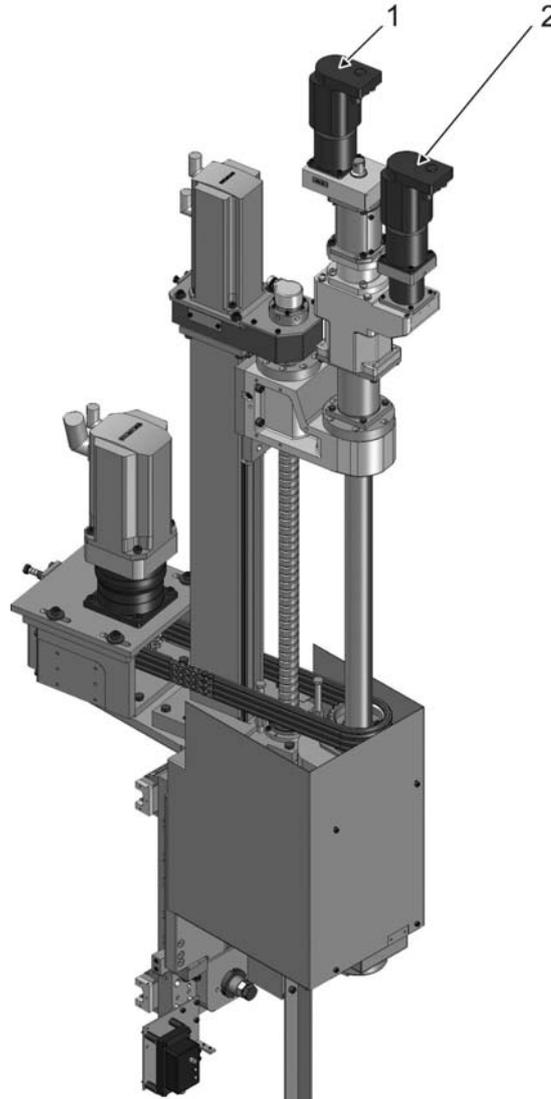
Spindleinheit VSM mit einer elektromechanisch-elektromechanischen Dreh-Druck Aufweitung
